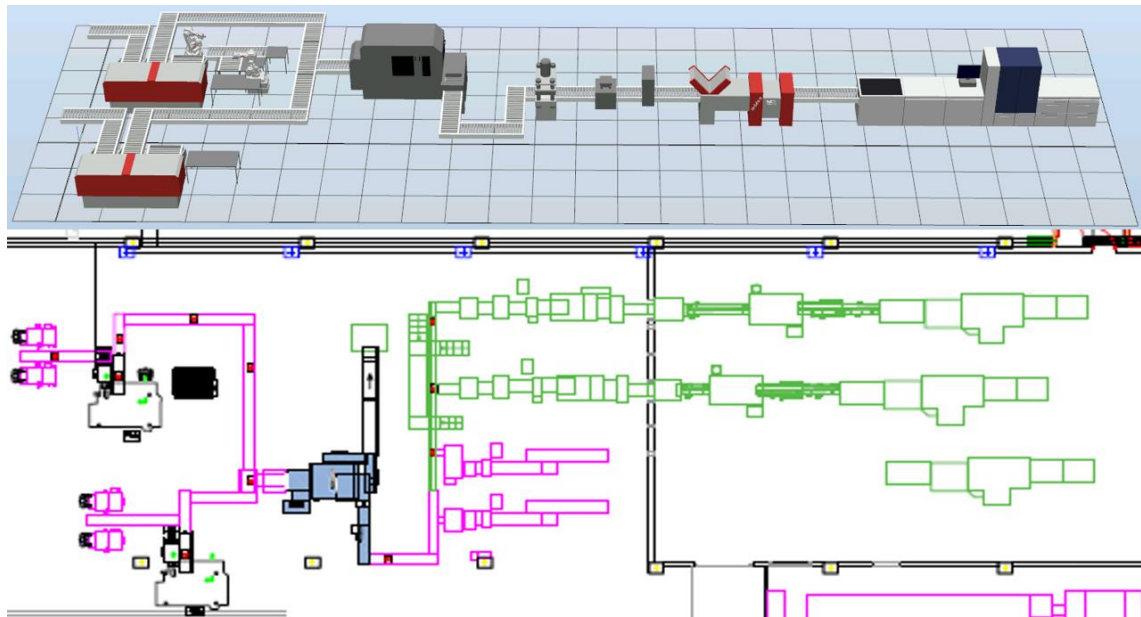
Plano de la planta y línea modelada en Robotstudio.
